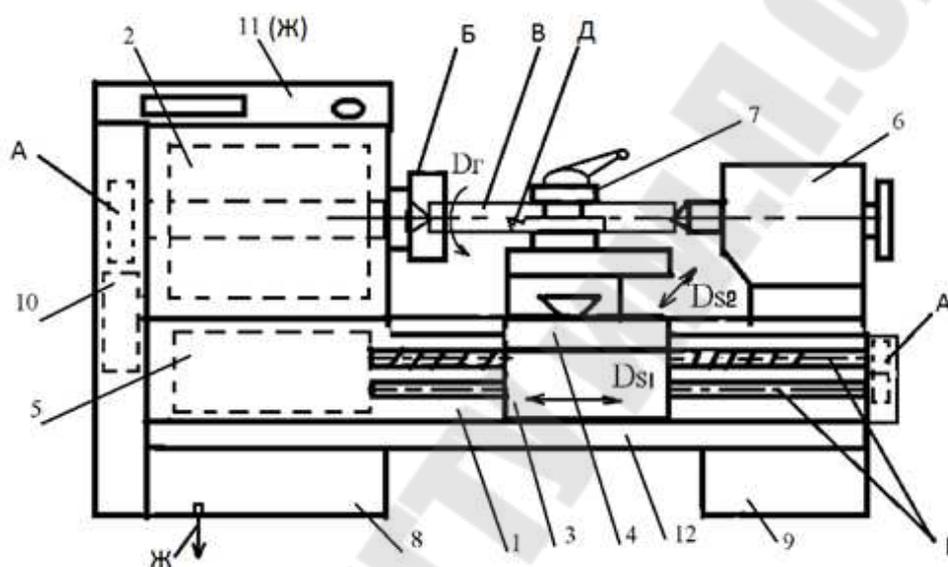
Устройство токарно-винторезного станка мод.1К62 и его опасные места (зоны)
